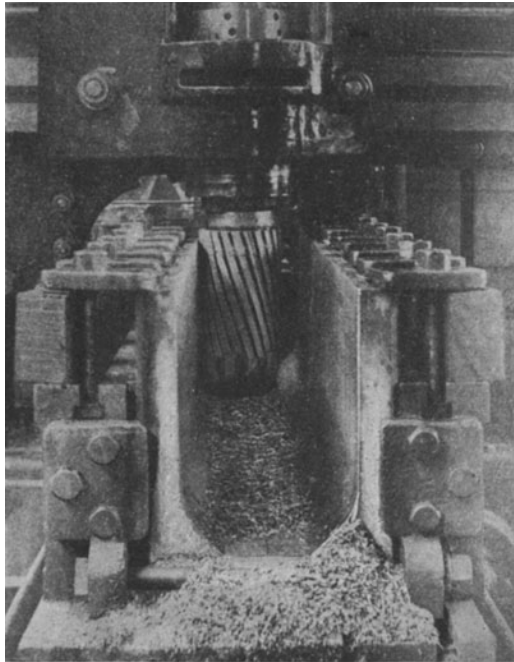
Bearbeitung von Achsbüchsen auf der Fräsmaschine.
